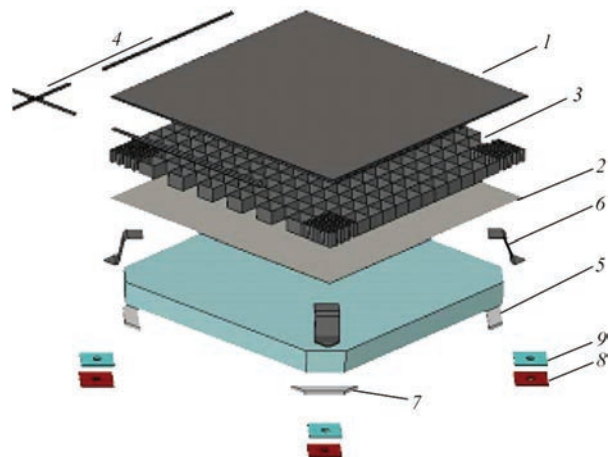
Общий вид плитки ТЗК: 1 — верхняя обшивка панели; 2 — нижняя обшивка панели; 3 — сотовый наполнитель; 4 — U-образные выштамповки; 5 — теплоизоляция; 6 — Z-образные металлические стойки системы крепления; 7 — фетровая подложка; 8 — демпфирующая прокладка из термостойкой резины; 9 — термомост
